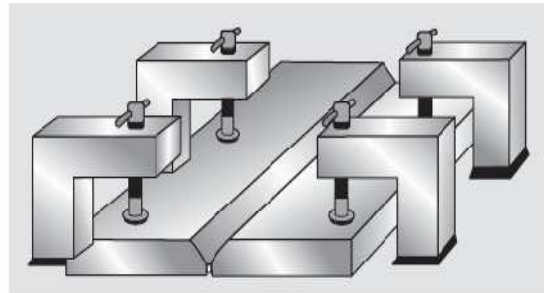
bridage pour soudage bout à bout [17]
